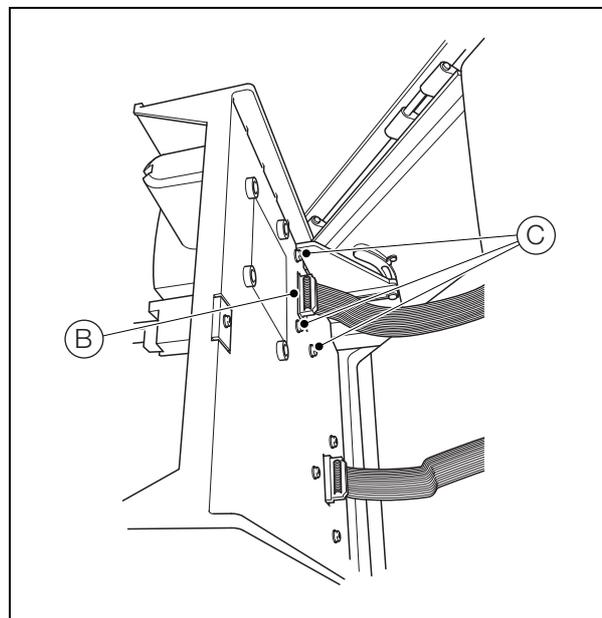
Ausbauen der Messzellenbaugruppe
